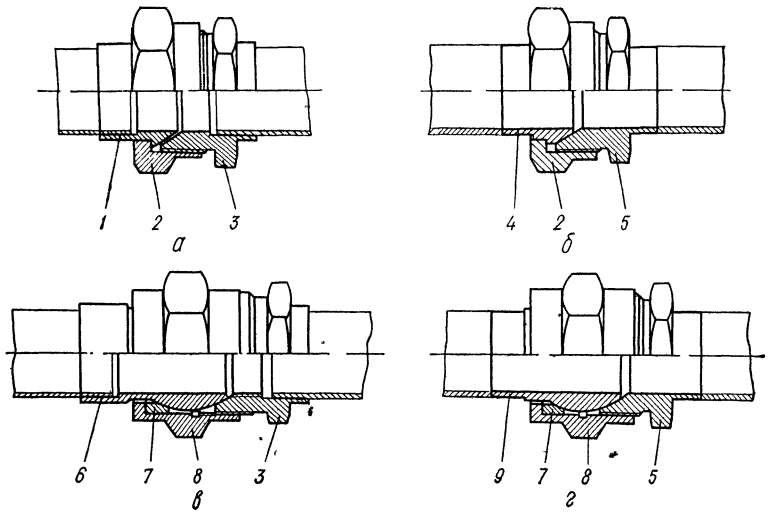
Полусферические припайное (а) и приварное (б), сферические припайное (в) и приварное (г) соединения по внутреннему конусу: 1 — ниппель полусферической припайной; 2 — гайка накидная для полусферических ниппелей; 3 — штуцер припайной; 4 — ниппель полусферический приварной; 5 — штуцер приварной; 6 — ниппель сферический припайной; 7 — кольцо упорное; 8 — гайка накидная для сферического ниппеля; 9 — ниппель сферический приварной.
